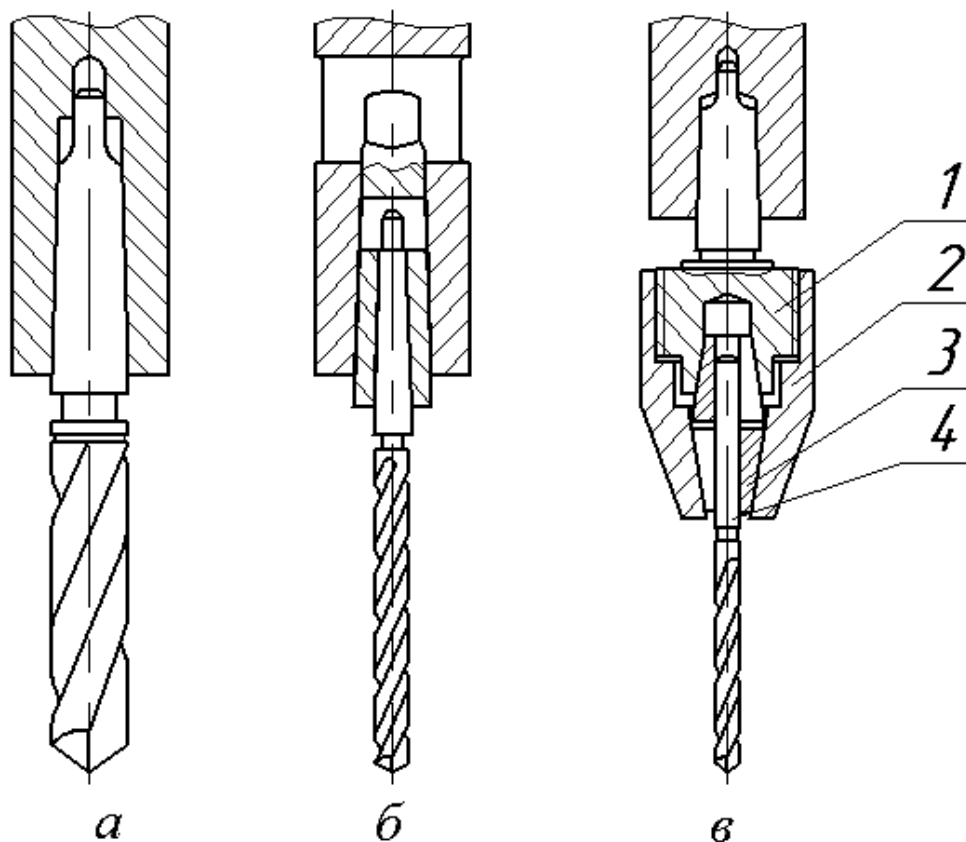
Способи закріплення інструмента на свердильних верстатах
